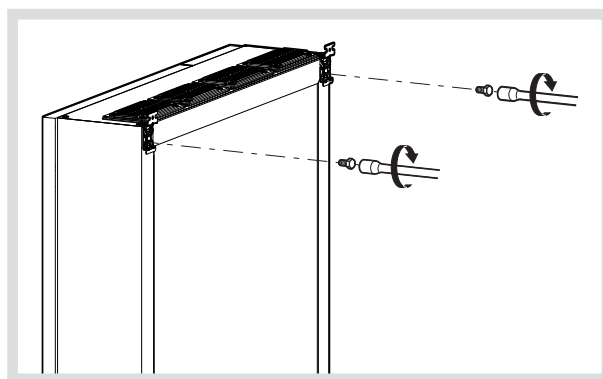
Montage Befestigungslaschen für Hängebefestigung
